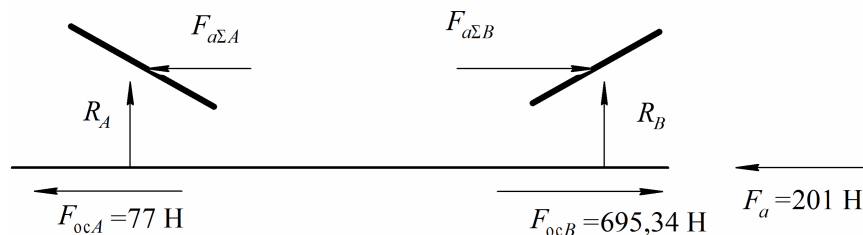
Схема нагружения быстроходного вала и подшипников
